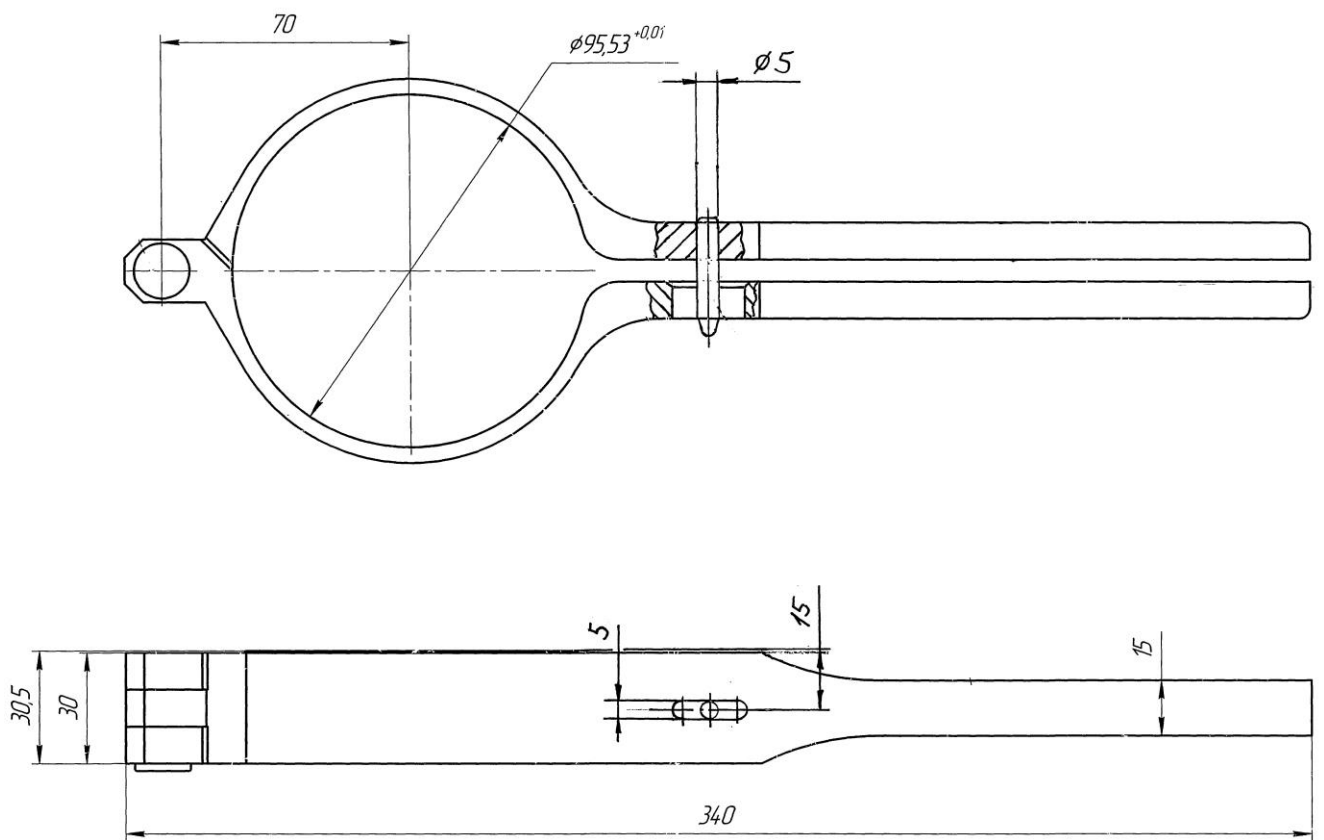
ЗМ 7820-4517 – Оправка для сжатия поршневых колец $\varnothing 95,5$ мм
